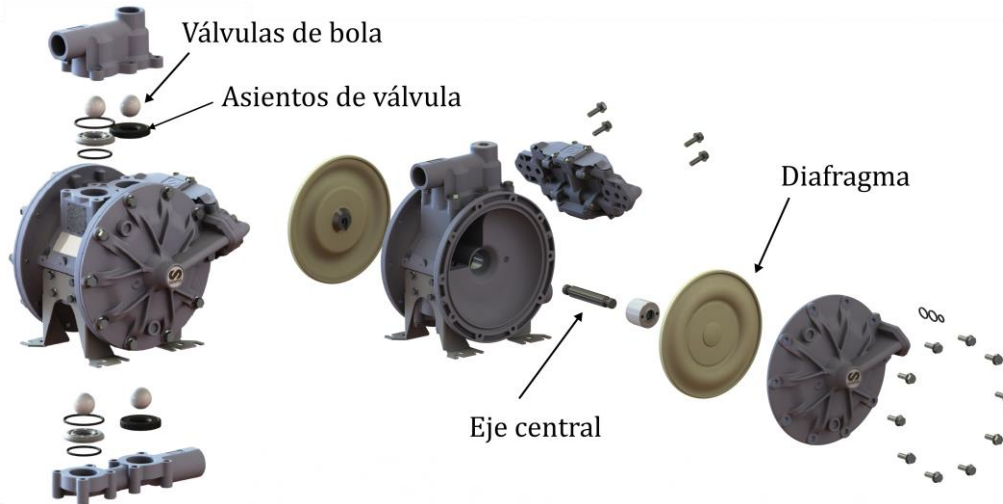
Despiece de los componentes principales de la bomba dúplex.
